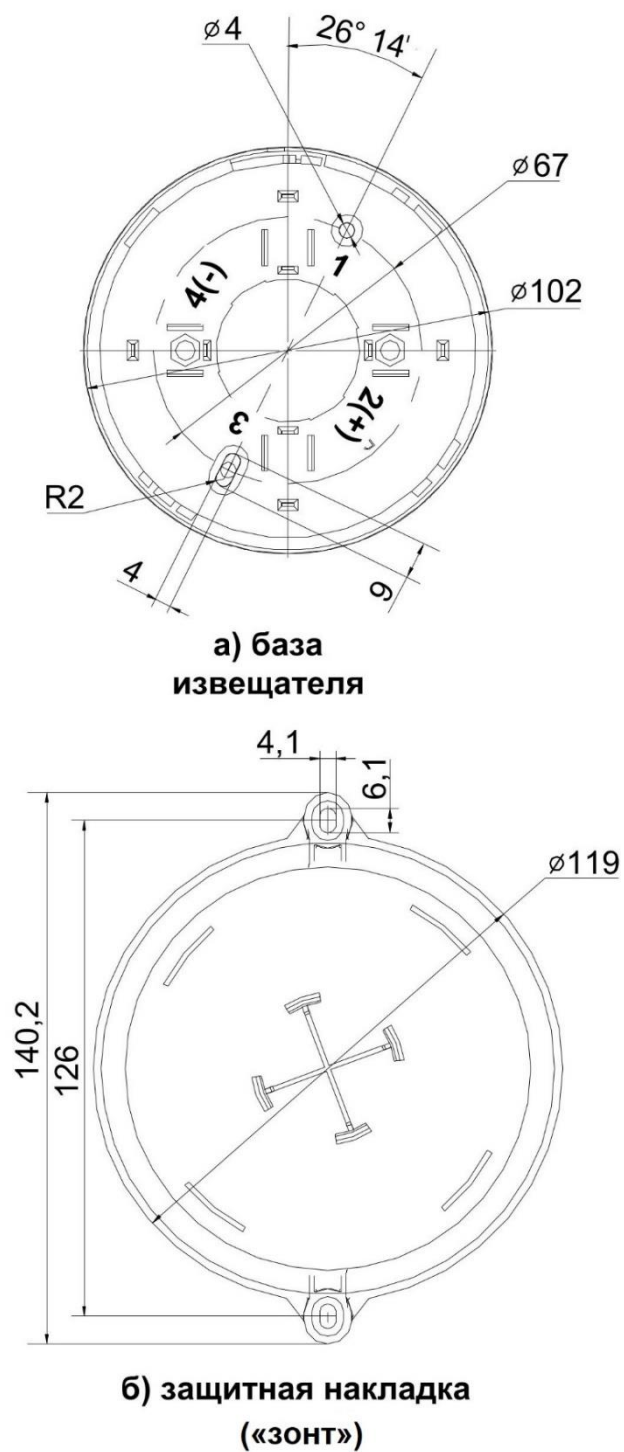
А2ДПИ. Габаритные и присоединительные размеры базы и защитной накладки «Зонт»
